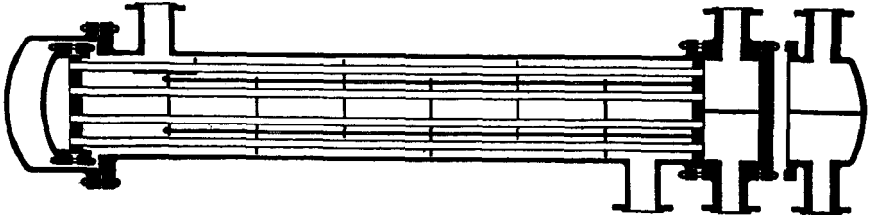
Intercambiador 1-2 de cabezal flotante. (Patterson Foundry & Machine Co.)
